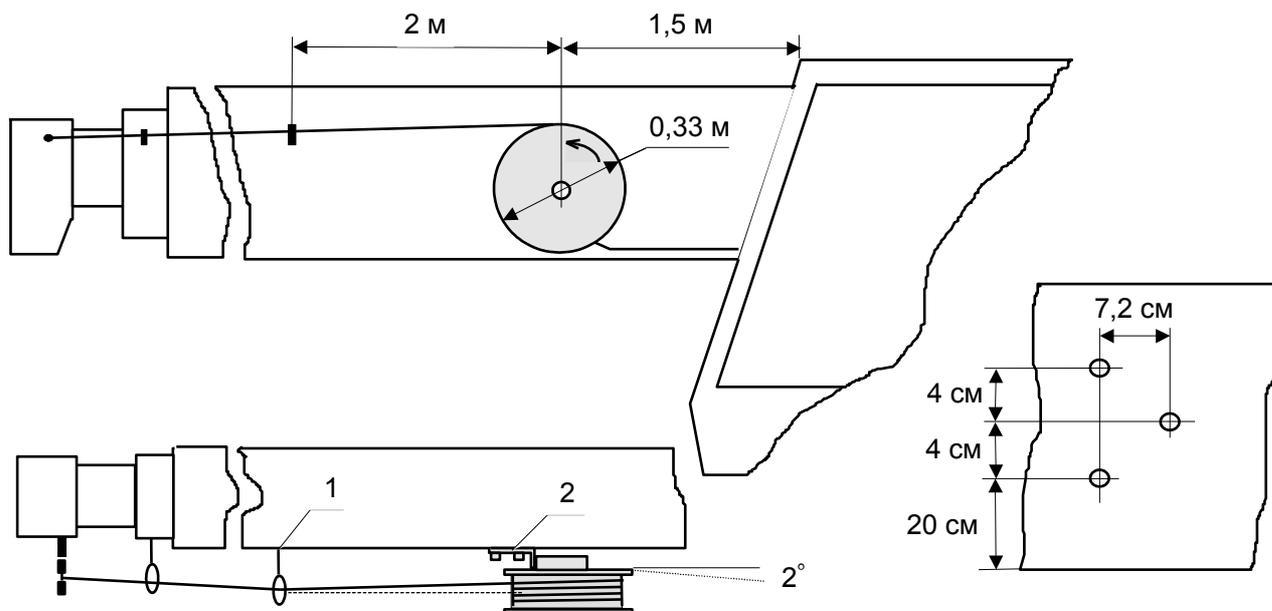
Установка датчика длины стрелы и разметка мест крепления
